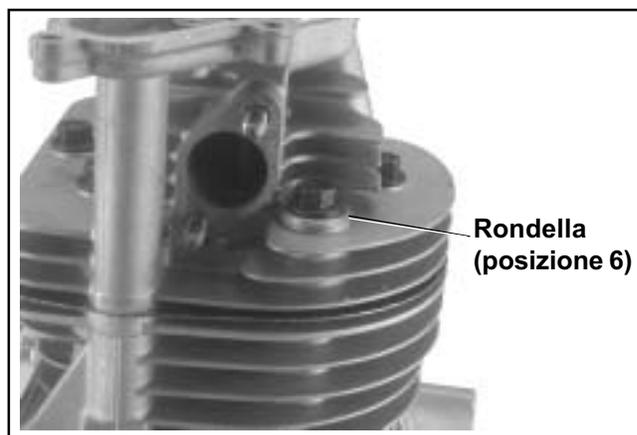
Installazione dei dispositivi di fissaggio della testata.
